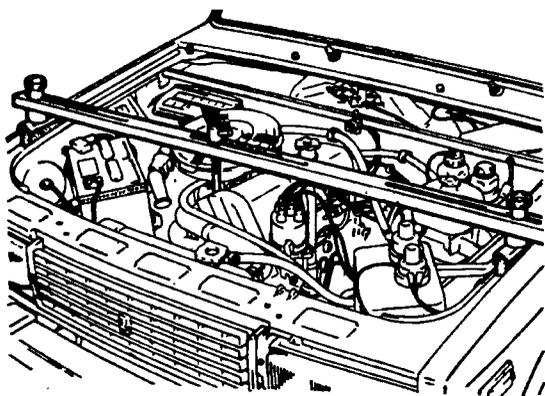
Установка траверсы А.70526 для поддержания двигателя при снятии поперечины передней подвески
